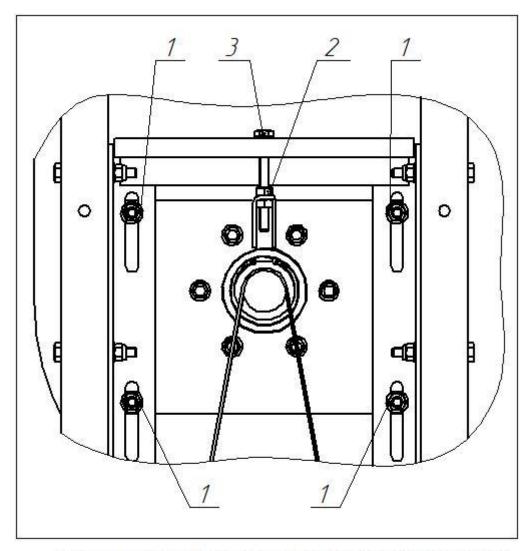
Регулировка натяжения ремня устройства вакуумного
